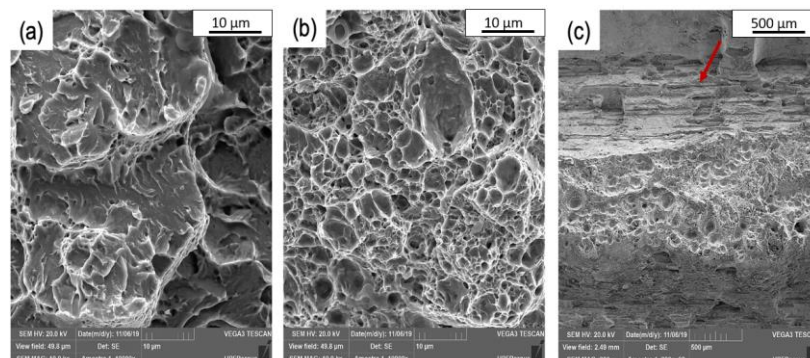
Microscopia óptica da superfície de fratura de amostras soldadas a laser após o teste de tração; (a) grande área com aparência facetada representando o aço 22MnB5; (b) pequena área com aparência facetada representando o aço modificado Nb-Mo
